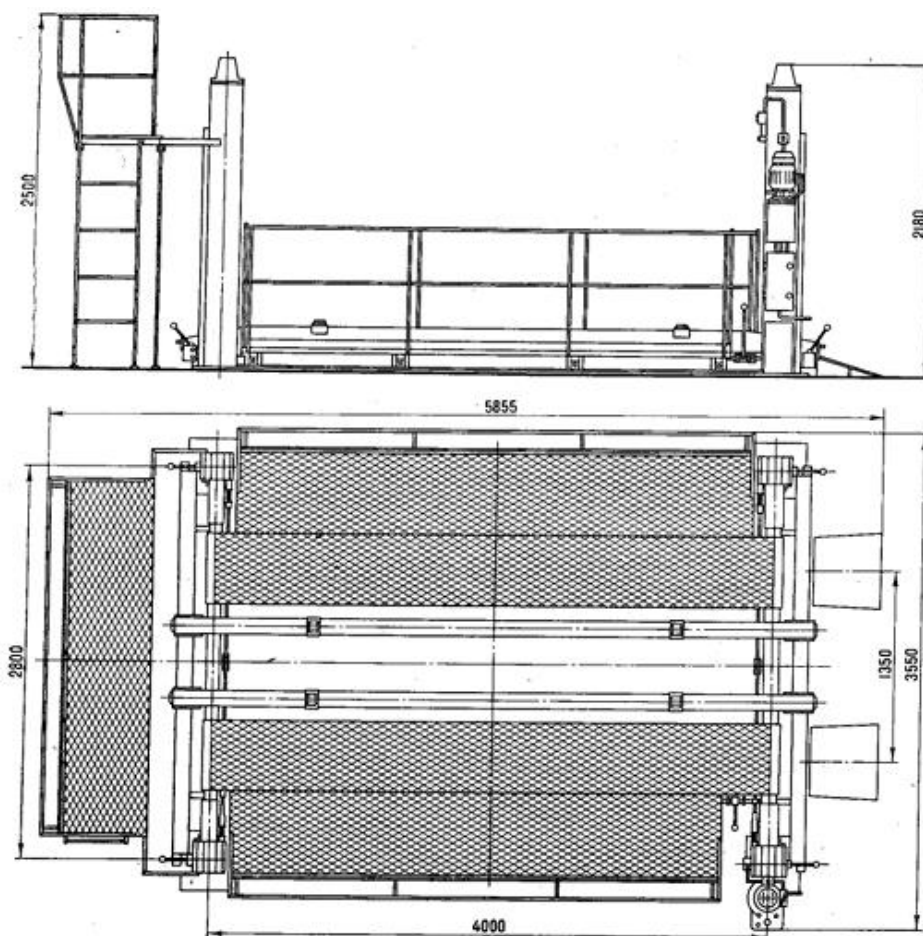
Чотирьохопорний підйомний стенд BELED-A
